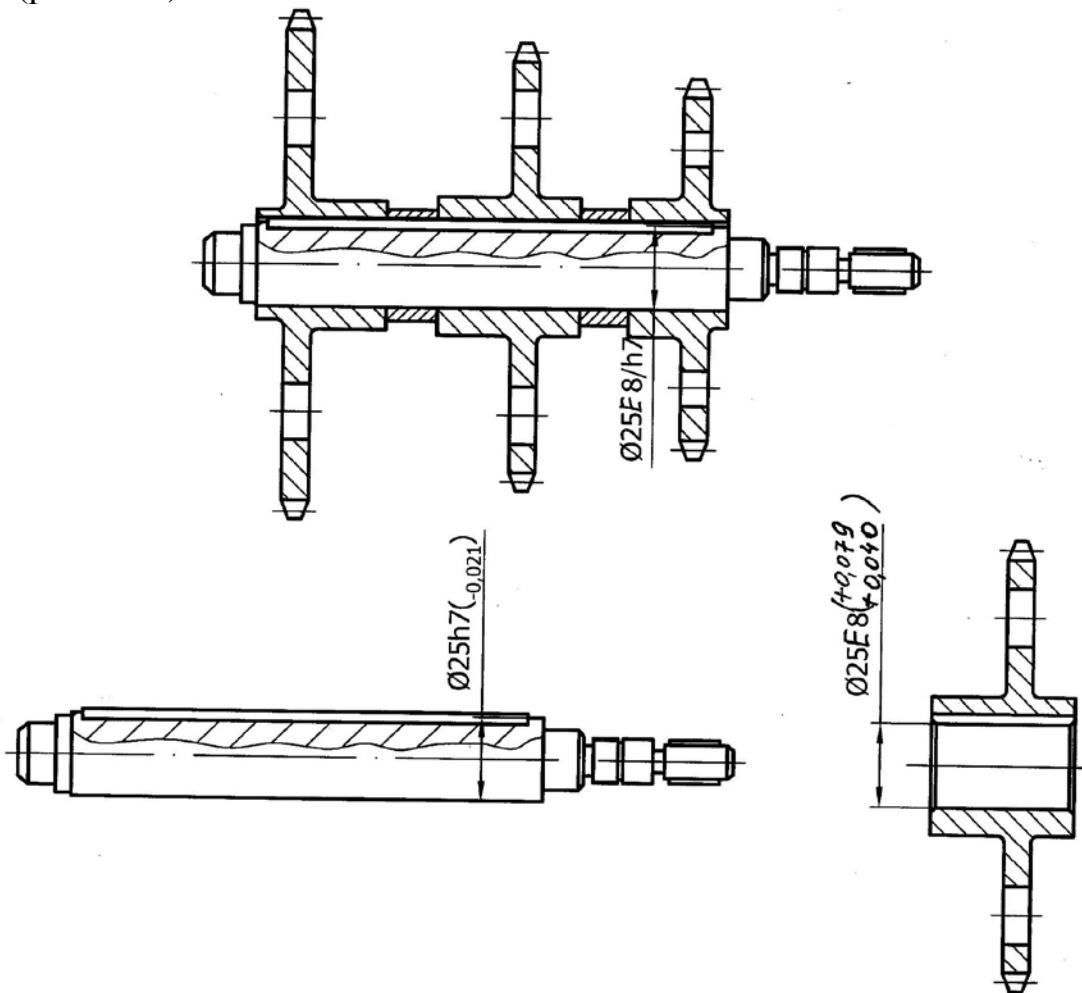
Посадка звездочек на вал при дополнительном креплении шпонкой в скоростной цепной коробке передач
